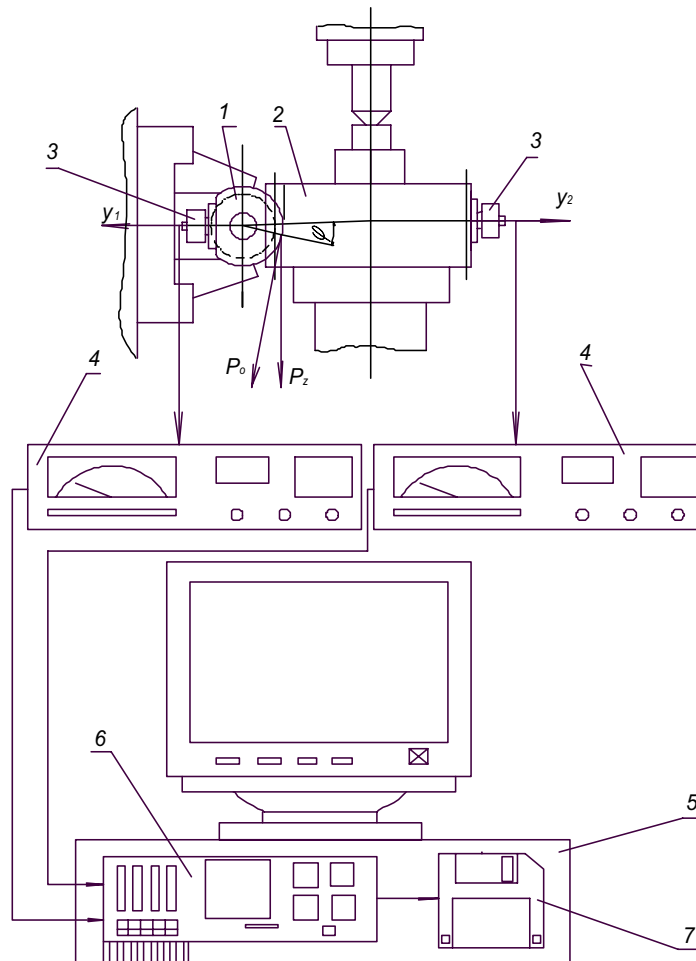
Схема вимірювання коливань у робочій зоні зубофрезерного верстата:
